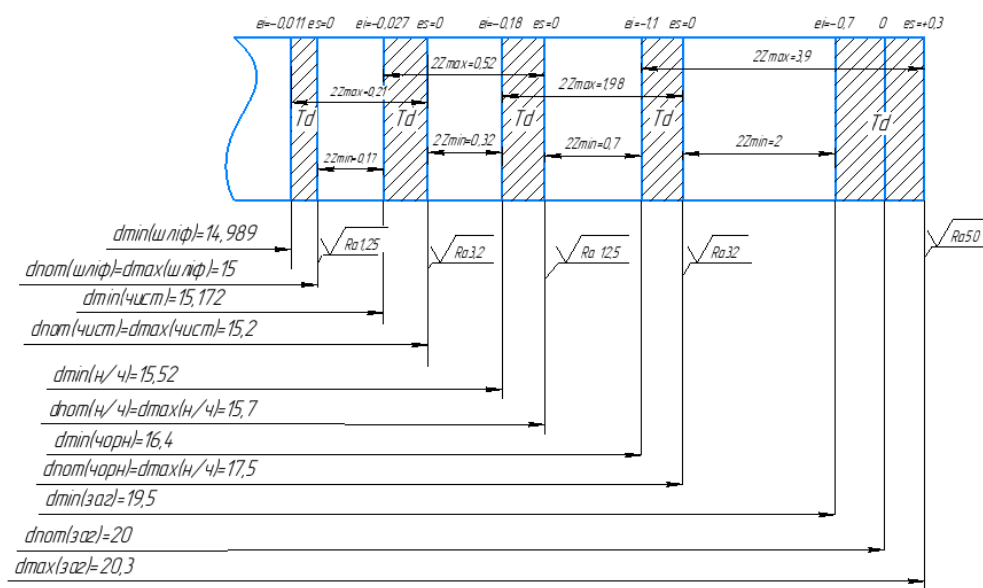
Схема розташування припусків і допусків на розмір
